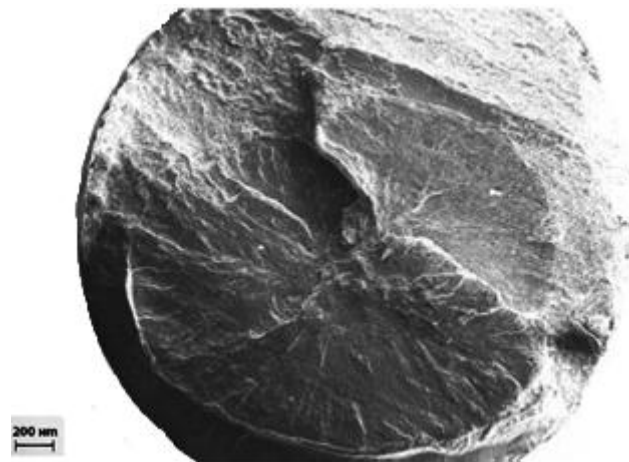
поверхность излома инструмента из сплава ВТЗ-1 при подповерхностном зарождении трещин
